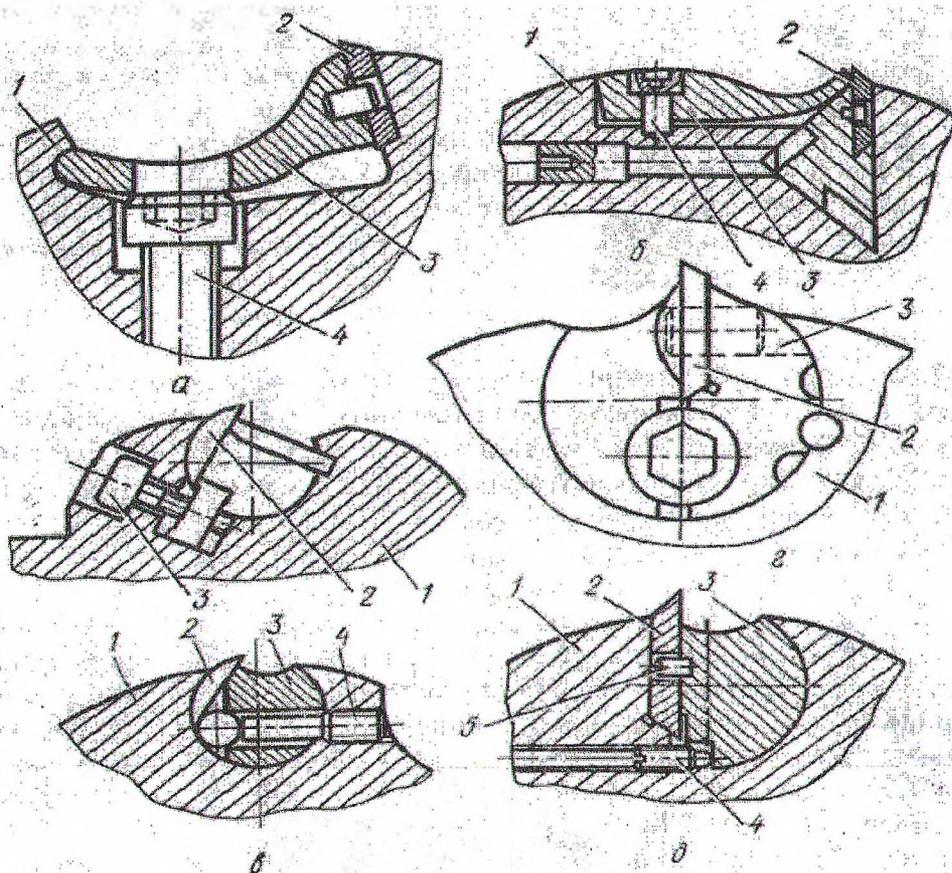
Фрезы с рычажной системой и базированием пластины: а, в, д – на площадке в корпусе; б, г – на отдельном элементе; 1 – корпус; 2 – пластина; 3 – рычажное устройство; 4 – винт; б – штифт
